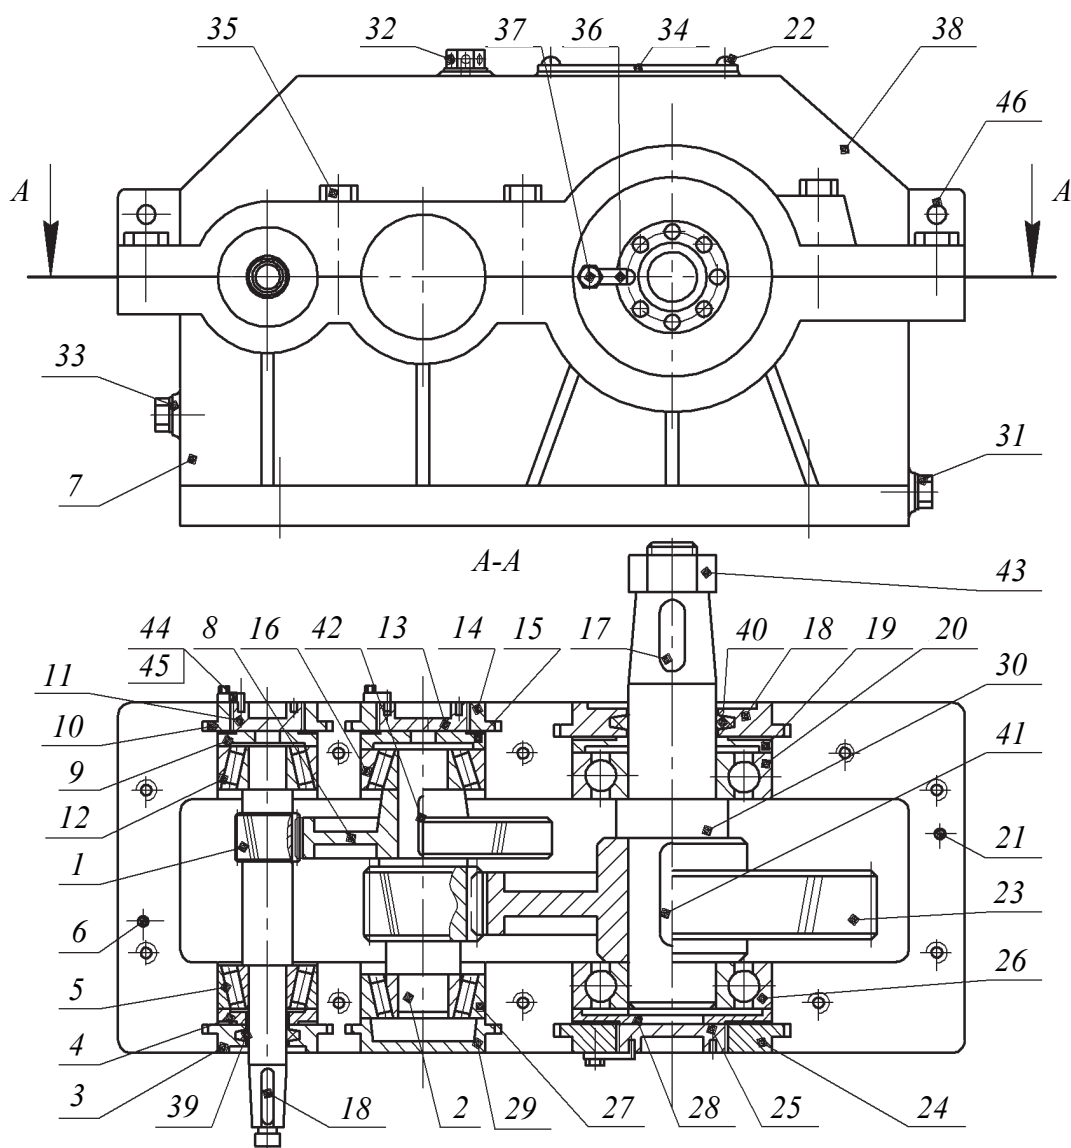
Конструкция цилиндрического двухступенчатого редуктора:
